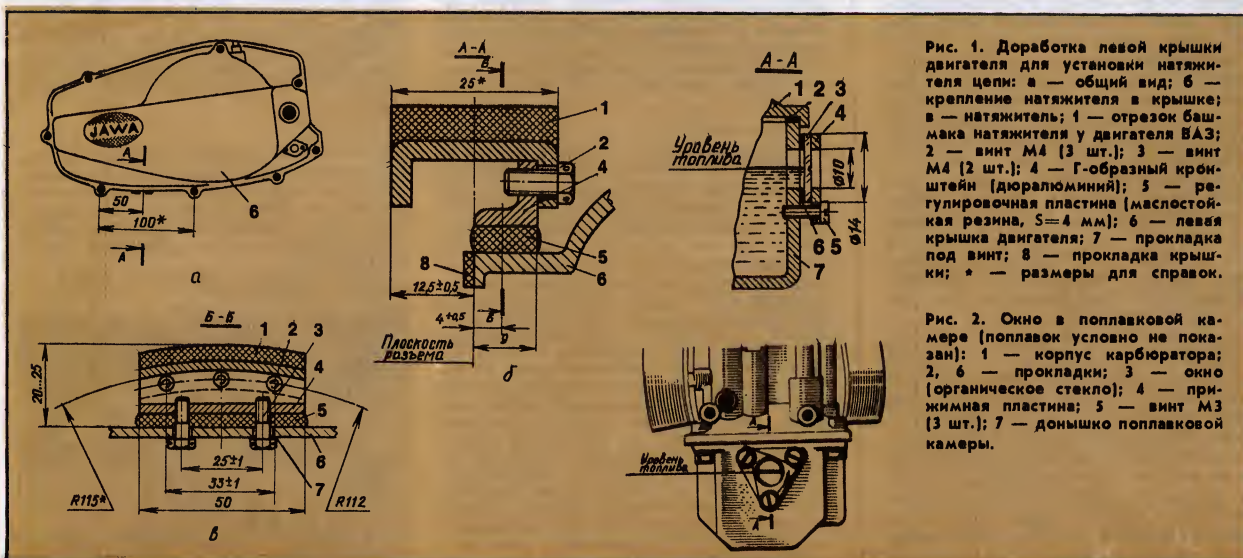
Доработка левой крышки двигателя для установки натяжителя цепи: а — общий вид; б — крепление натяжителя в крышке; в — натяжитель; 1 — отрезок башмака натяжителя у двигателя ВАЗ; 2 — винт М4 (3 шт.); 3 — винт М4 (2 шт.); 4 — Г-образный кронштейн (дюралюминий); 5 — регулировочная пластина (маслостойкая резина, S=4 мм); 6 — левая крышка двигателя; 7 — прокладка под винт; 8 — прокладка крышки; * — размеры для справок.
